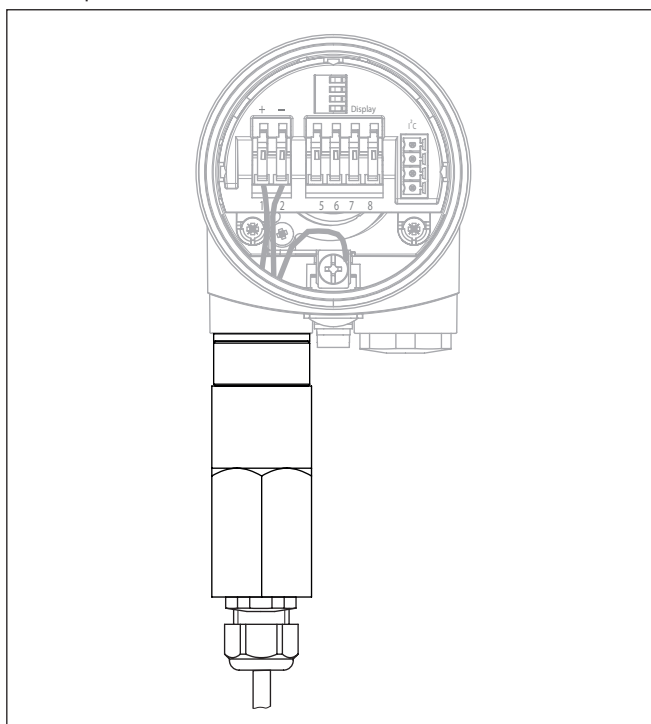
Protezione di sovratensione B63-48, B63-32 dopo installazione e collegamento
